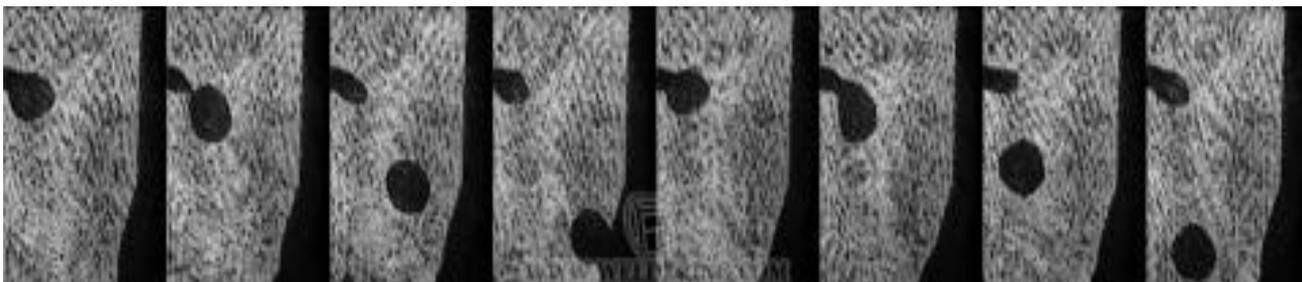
Потери металла при сварке в вертикальном положении [48]
